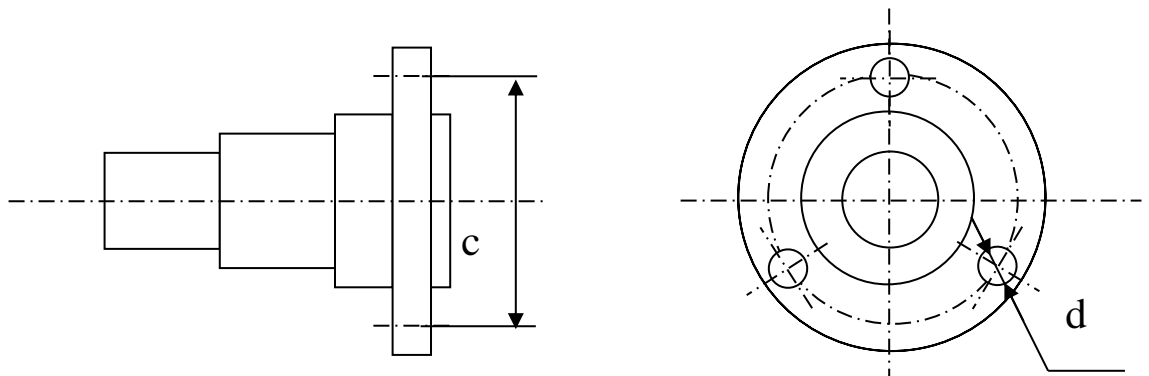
Схема для розрахунку болтового з'єднання
